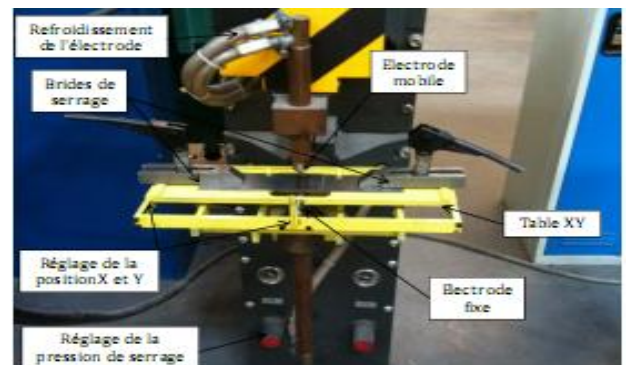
Machine à souder par point avec montage de mise en position de l'éprouvette.
